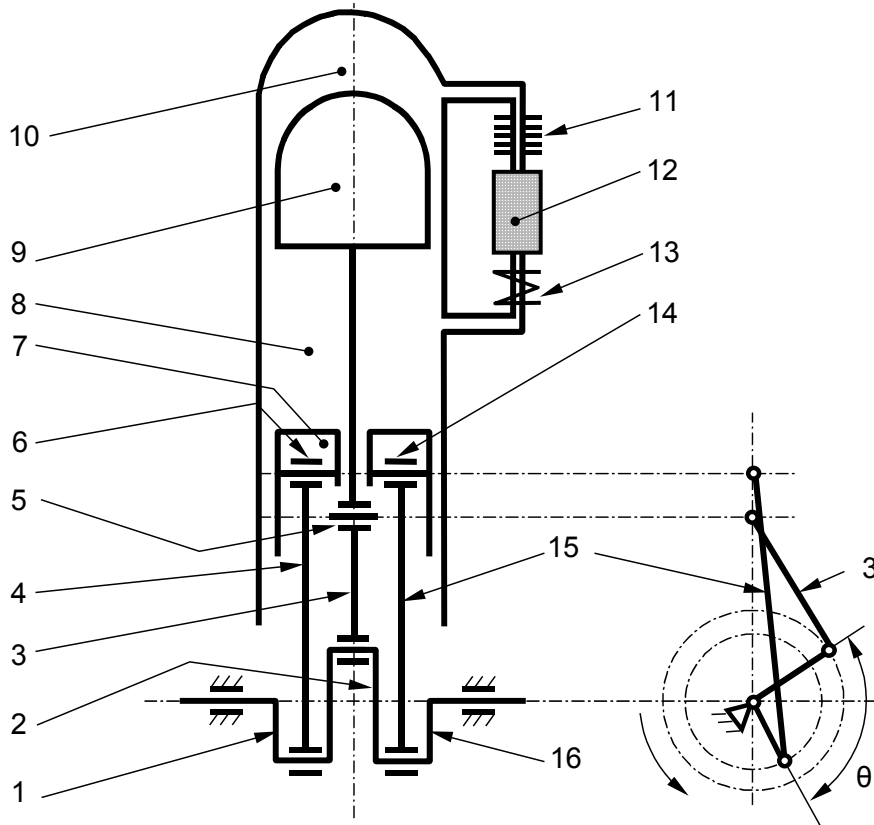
Motor Stirling de tip „beta“ cu mecanism motor compus din trei mecanisme bielă - manivelă: 1 și 16 - coturi laterale; 2 - cot central; 3 - biela pistonului împingător; 4 și 15 - biebele pistonului motor; 5, 6 și 14 - bolțuri; 7 - pistonul motor; 8 - camera de comprimare; 9 - pistonul împingător; 10 - camera de destindere; 11 - încălzitor; 12 - regenerador; 13 - răcitor
